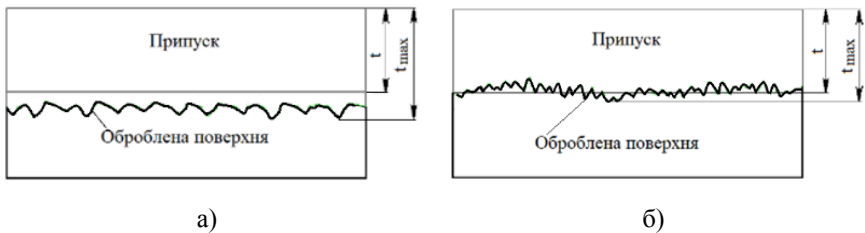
Профілограми поверхонь після зустрічного (а) та попутного (б) фрезерування
